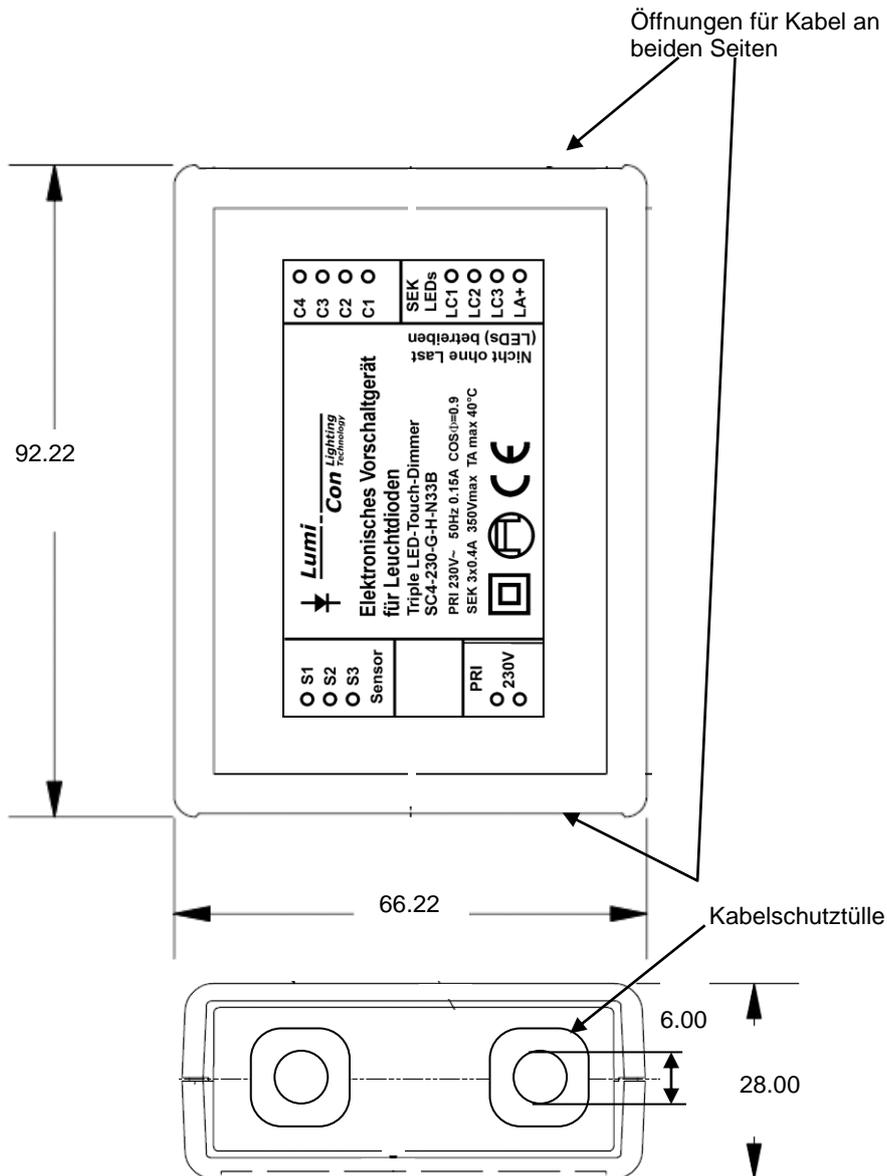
Dimmers, Gehäuseversion, Masse in mm
